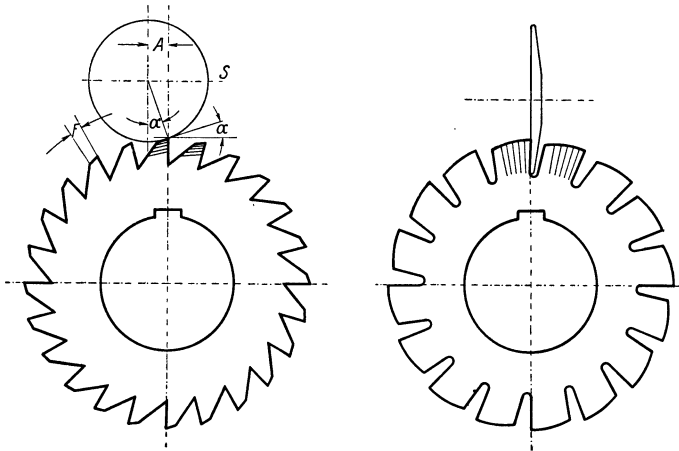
u. 5. Gefräster und hinterdrehter Fräser.
